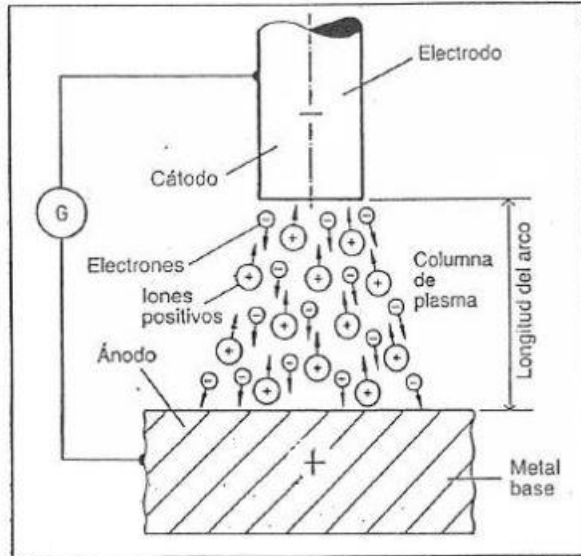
Soldadura SMAW (Shield Metal Arc Welding)
